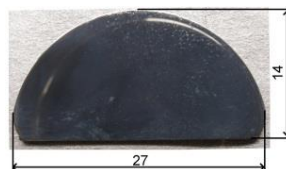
Внешний вид углеситалловой створки ИКС
